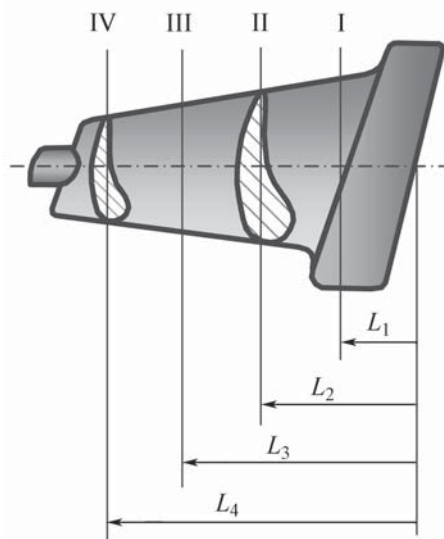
Схема расположения контрольных сечений I, II, III, IV на штамповке лопатки:
